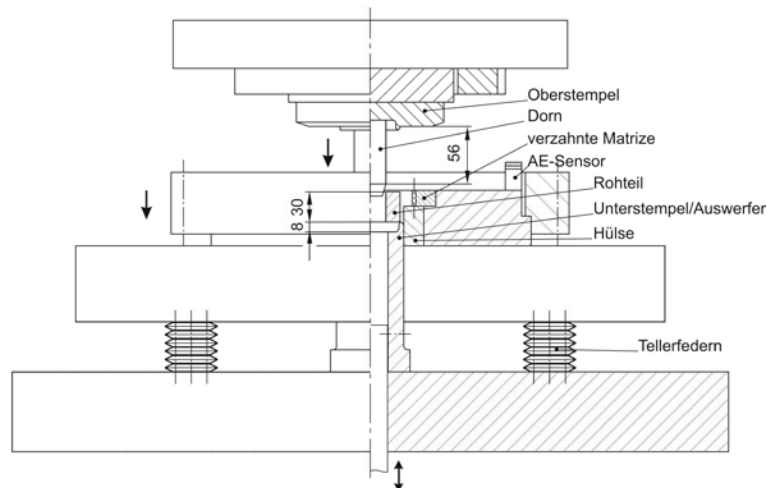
Werkzeugsystem für das Präzisionsschmieden von schrägverzahnten Zahnrädern [2]
